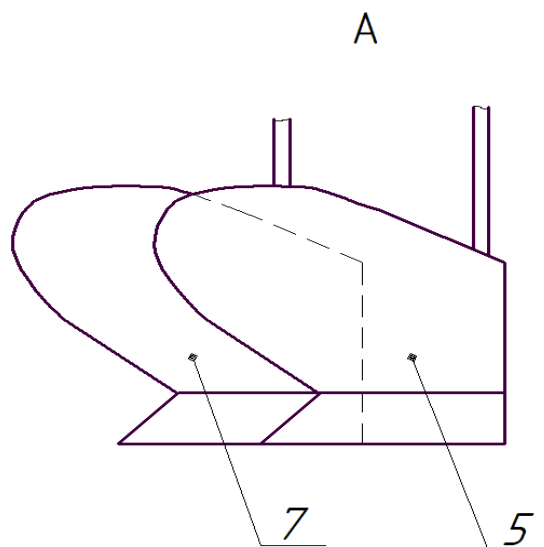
Вариант взаимного расположения первого (5) и дополнительного (7) рабочих корпусов (вид спереди)
